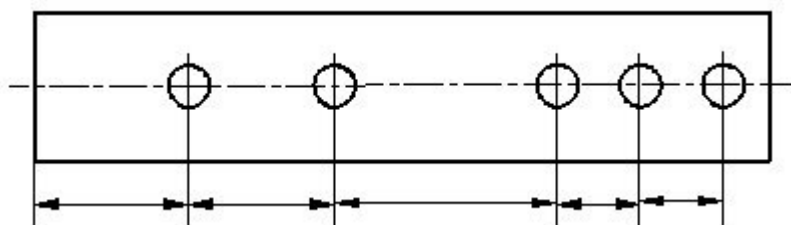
Примеры нанесения размеров цепочкой
